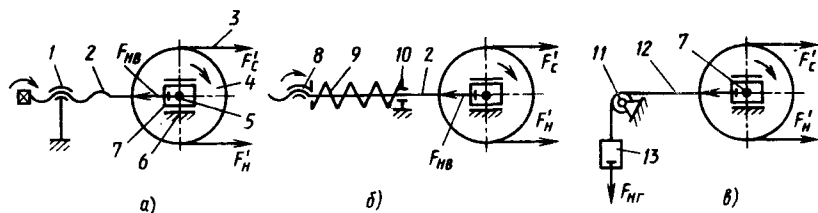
Схемы натяжных устройств ленточного конвейера: а — винтовое; б — винтовое с пружиной; в — грузовое
